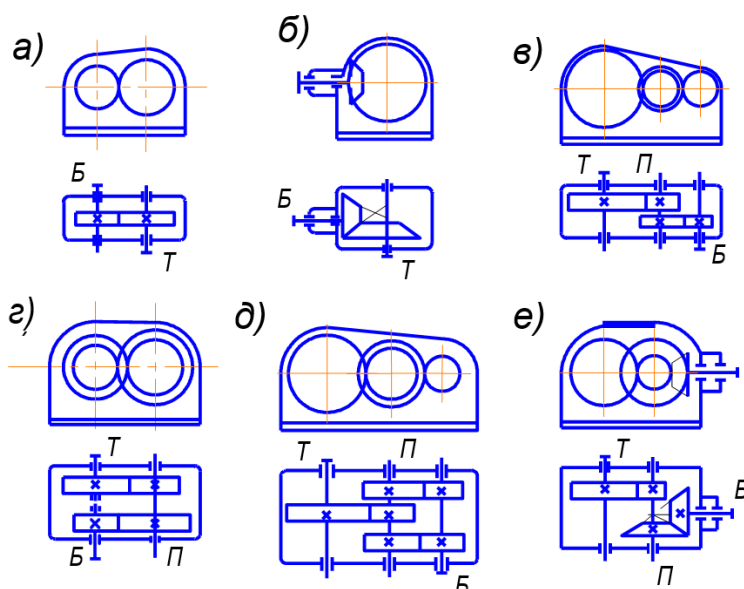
Кинематические схемы зубчатых редукторов
